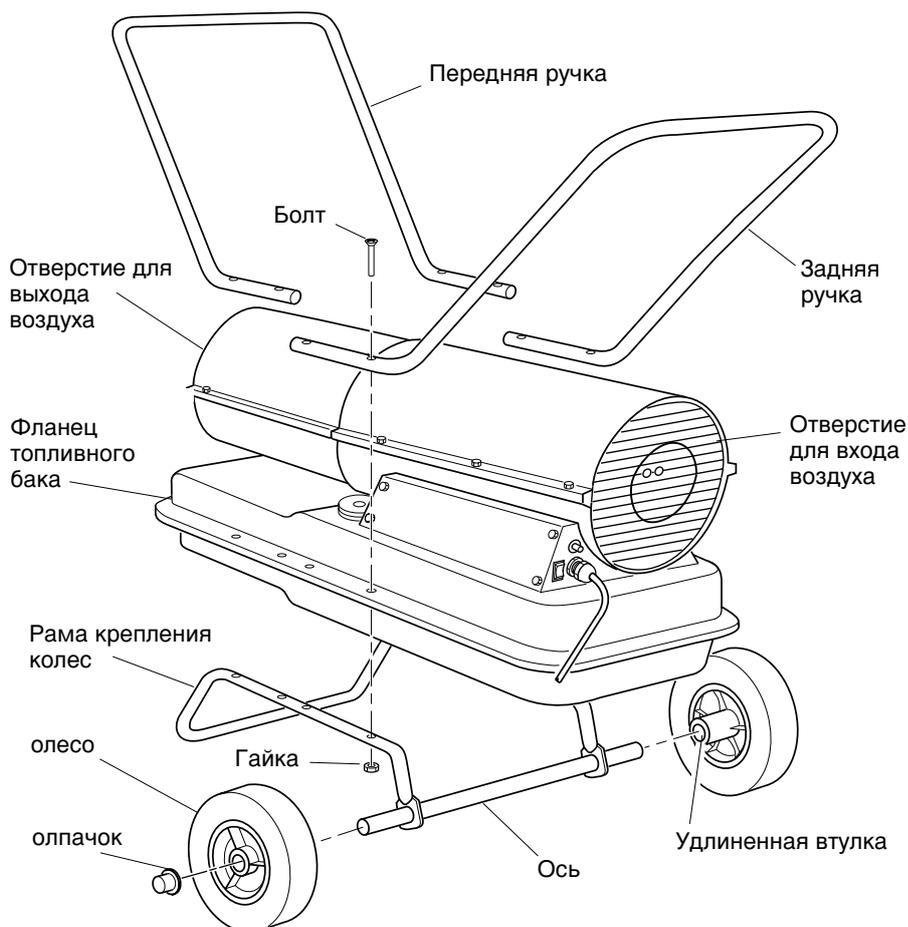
Сборка колес и ручек; только для нагревателей мощностью 29 и 44 кВт
